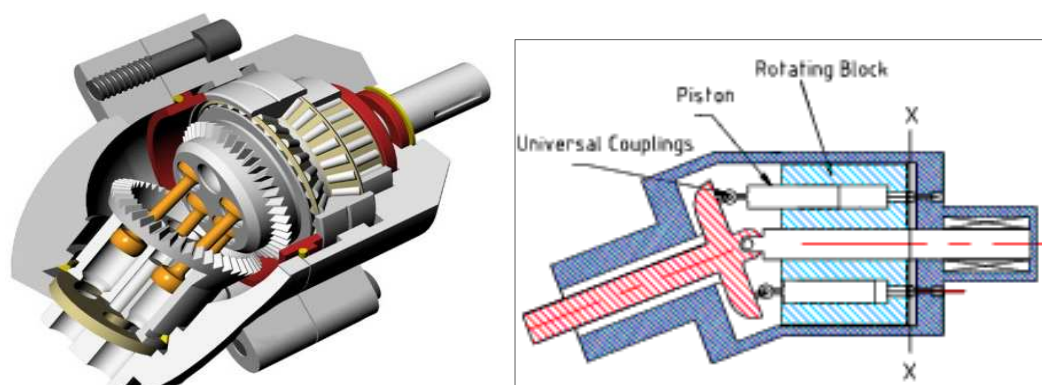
Schémas de deux différentes techniques pour mouvoir les pistons.
